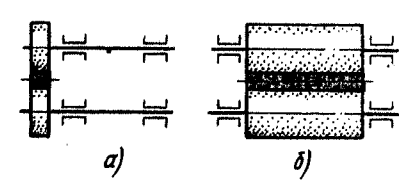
Расположение шлифовального и ведущего кругов на бесцентрово-шлифовальных станках
